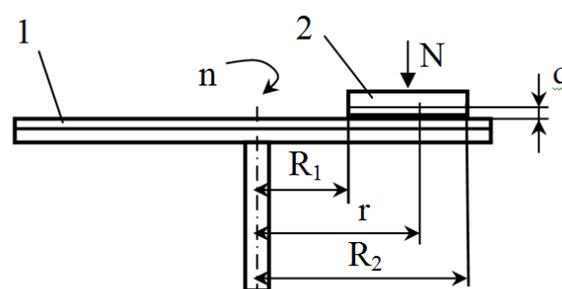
Схема абразивной обработки карбидокремниевой пластины
